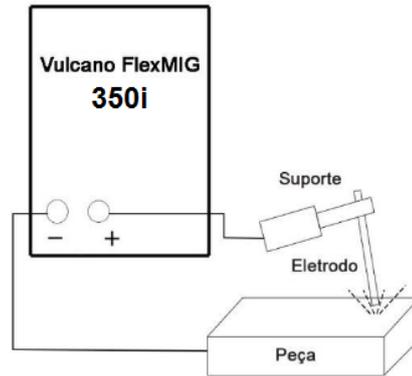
Conexão negativa para soldagem com eletrodo revestido
